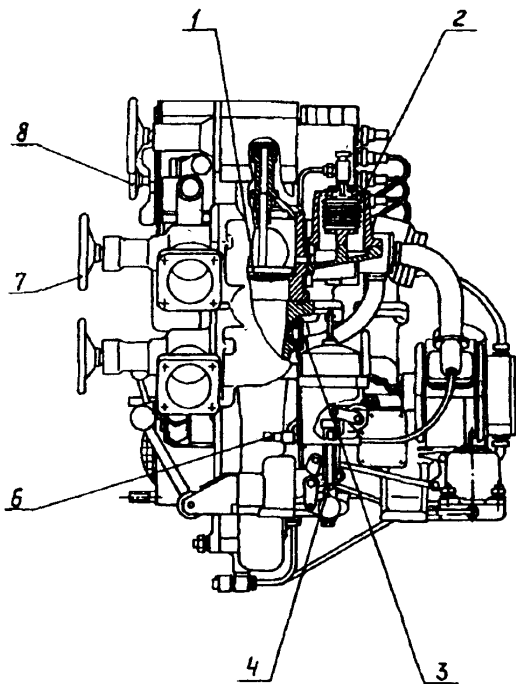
Насос центробежный пожарный комбинированный НЦПК-40/100-4/400:
